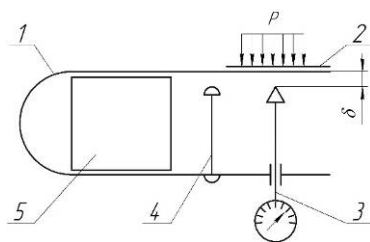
Схема вимірювального пристрою: 1 – скоба; 2 – каретка; 3 – вимірювальний пристрій; 4 – запобіжний пристрій; 5 – буферна прокладка.
